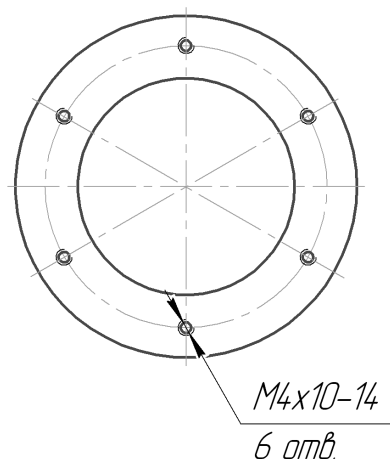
Схема сверления отверстий на гайке для крепления датчика
